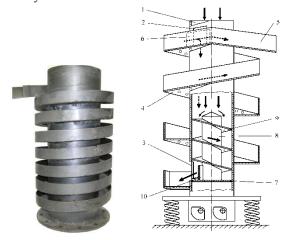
Подъемный винтовой вертикальный вибрационный СНД (патент РФ 2286203): 1 — несущая цилиндрическая колонна; 2 — верхнее окно для рециркуляции; 3 — нижнее окно; 4 — винтовой перфорированный лоток; 5 — выпускной патрубок; 6 — рассекатель; 7 — дно загрузочного бункера; 8 — цилиндрическая вставка; 9 — спиральная лопасть; 10 — направляющая заслонка
